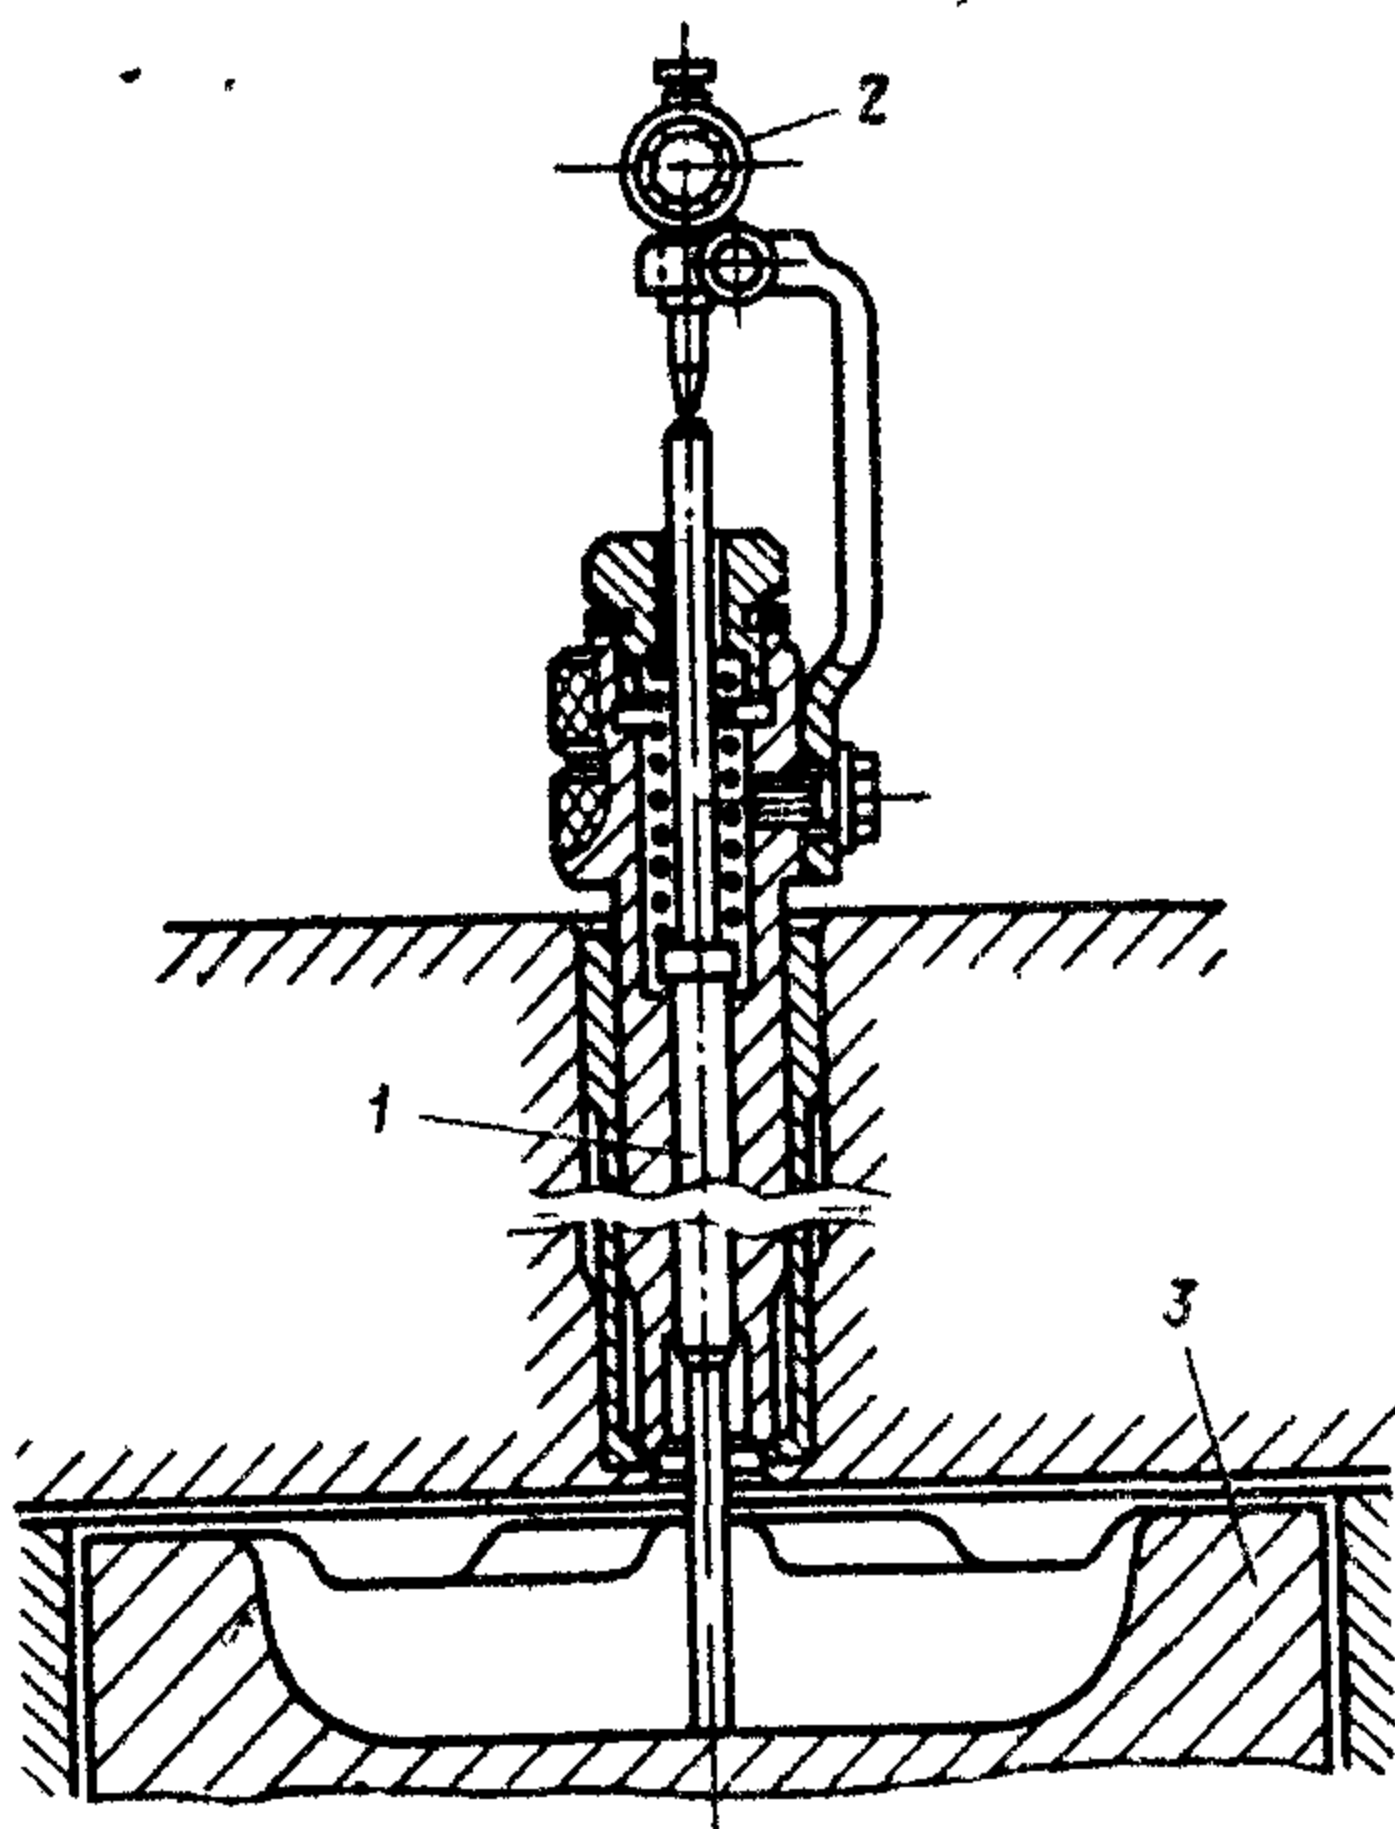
Регляж (приспособление для установки поршня в в.м.т.)
